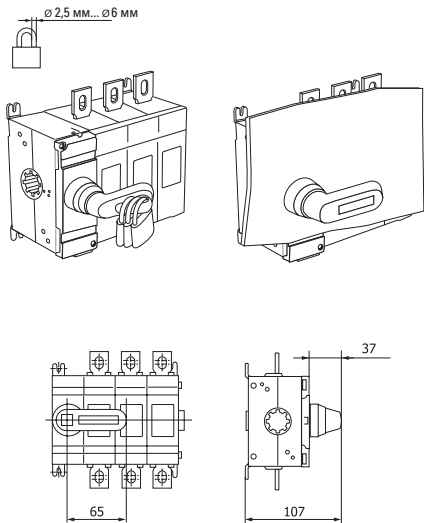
Установка рукоятки управления прямой установки 160-250 А
